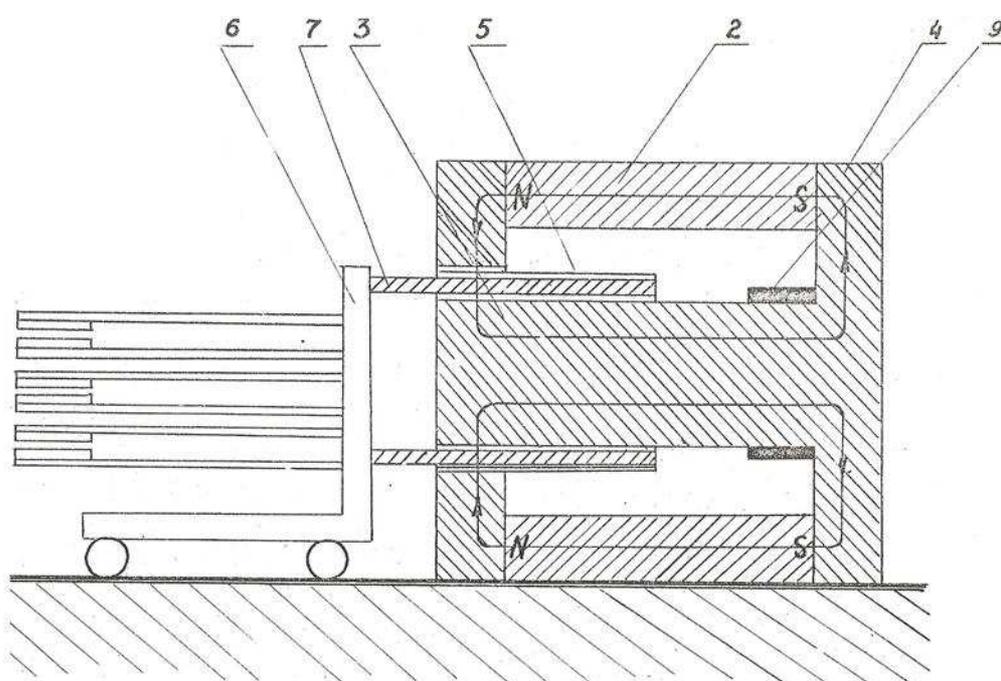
Линейный двигатель постоянного тока для возвратно-поступательного движения
